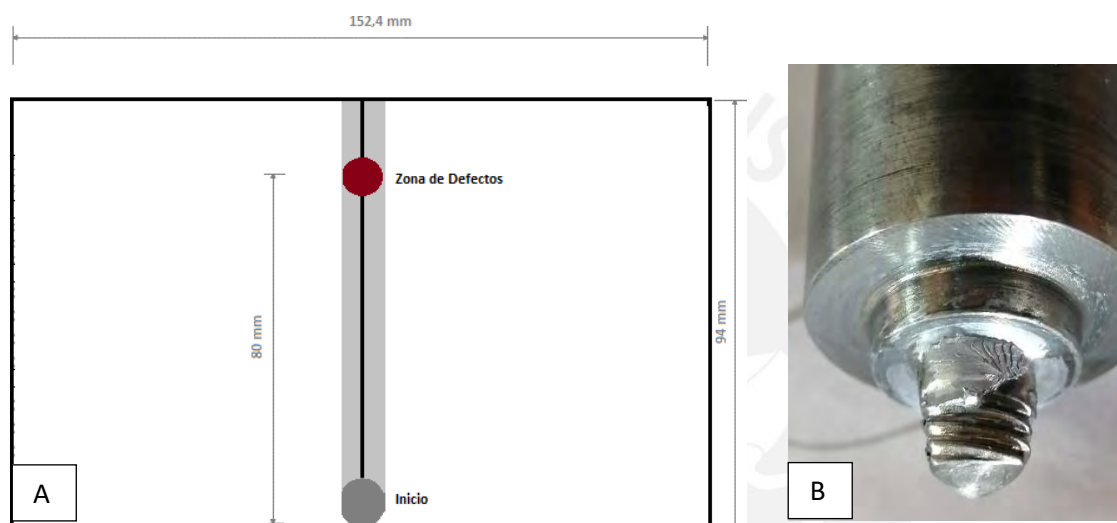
A) Esquema de zona de defectos vista superficial del cordón de soldadura B) . Pin MX trivex Posterior soldeo longitud de 95 mm a 1800 RPM x 40 mm/min.
